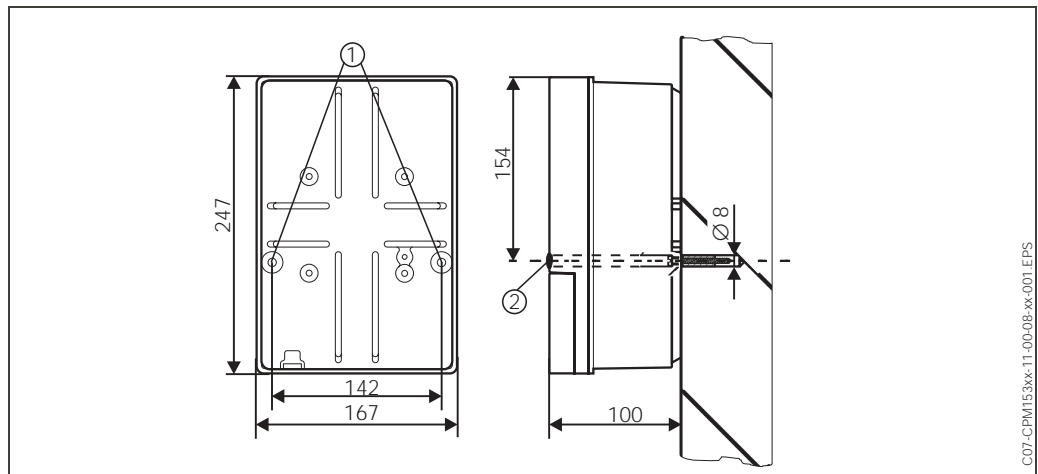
Dimensioni per il montaggio a parete: viti di fissaggio: dia. 6 mm
